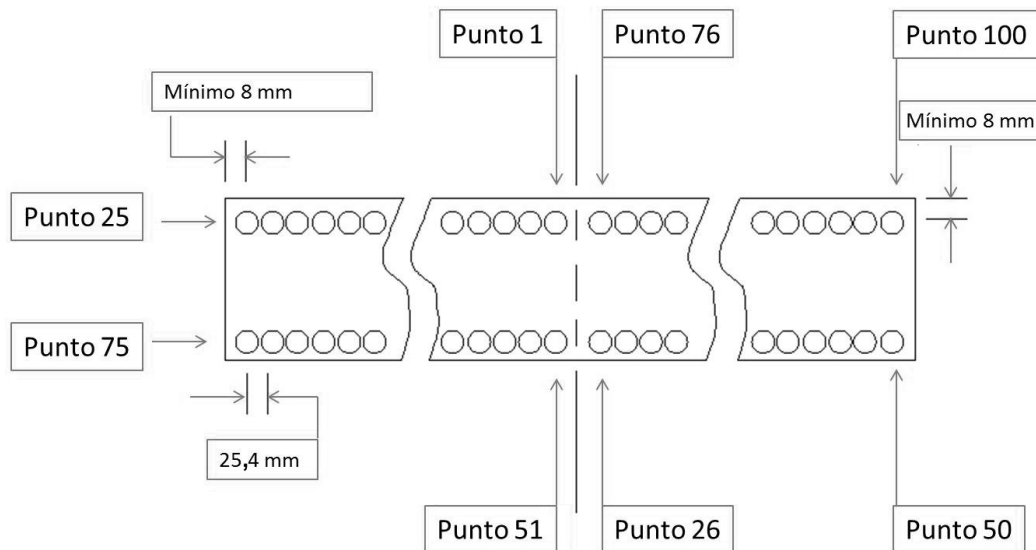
La secuencia de soldadura en el par de chapas.
